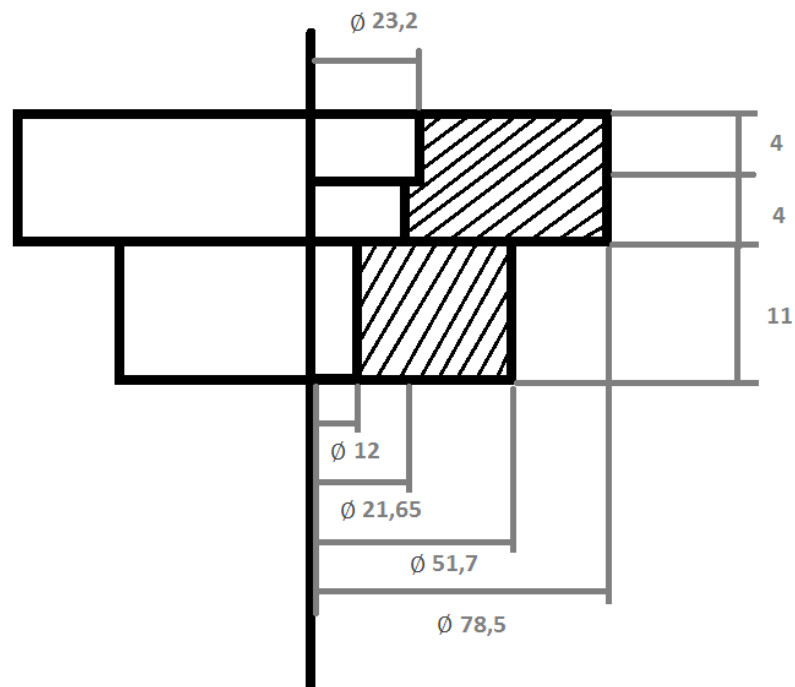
Dimensiones técnicas de la pieza de acoplamiento del collarín.
